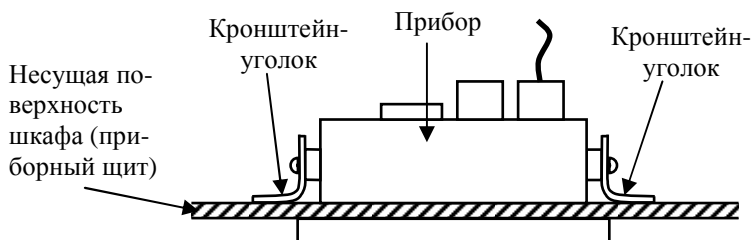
Установка прибора в шкаф/приборный щит (вид сверху)
